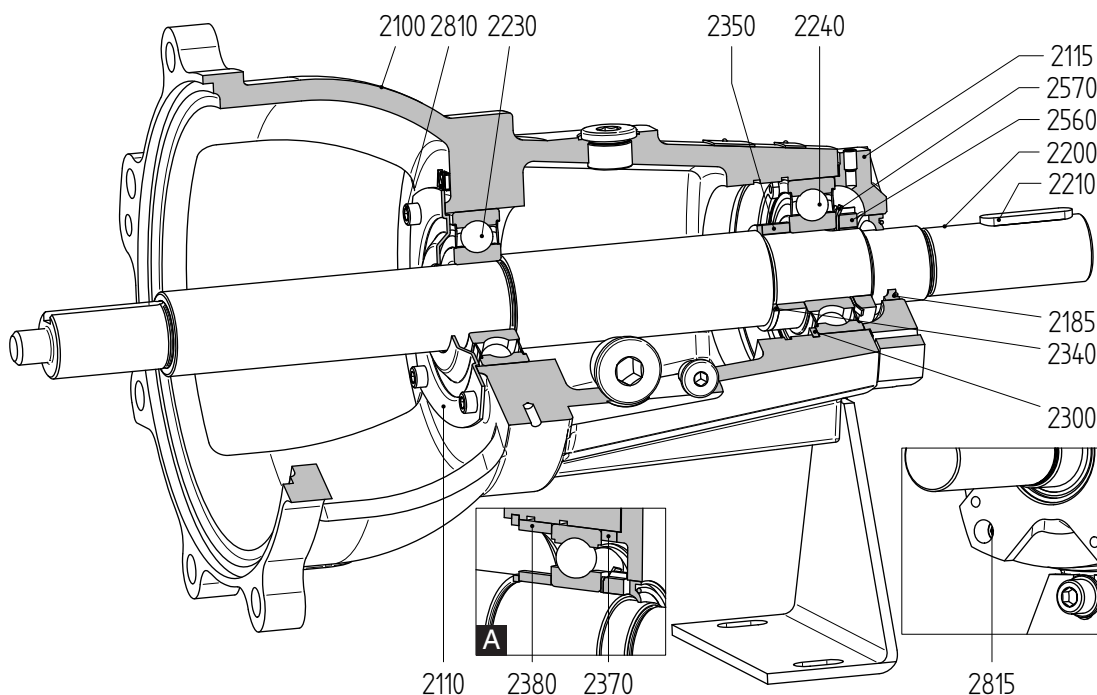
轴承 L1（标准，润滑脂润滑）（A = 轴承组 3）。
